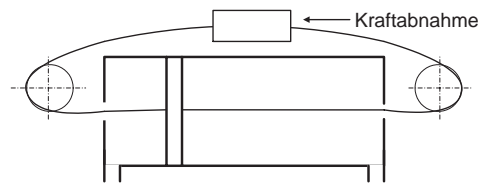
Zylinder ohne Kolbenstange (Symbol nicht genormt)
